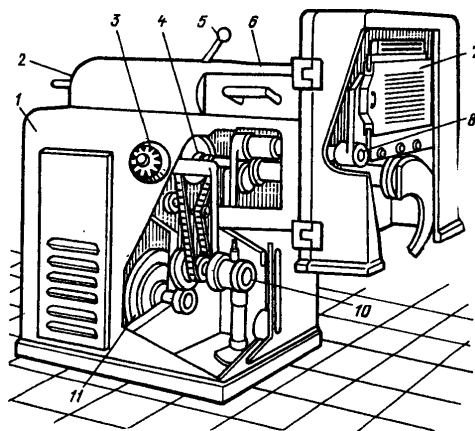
Горизонтальна гідравлічна шпигорізка ГГШМ: 1 – станина; 2 – кожух гідроциліндра; 3 – регулятор подачі шпику; 4 – привід ножового валу та ексцентрика; 5 – рукоятка включення; 6 – камера для шпику; 7 – різальний механізм; 8 – гойдаючийся
